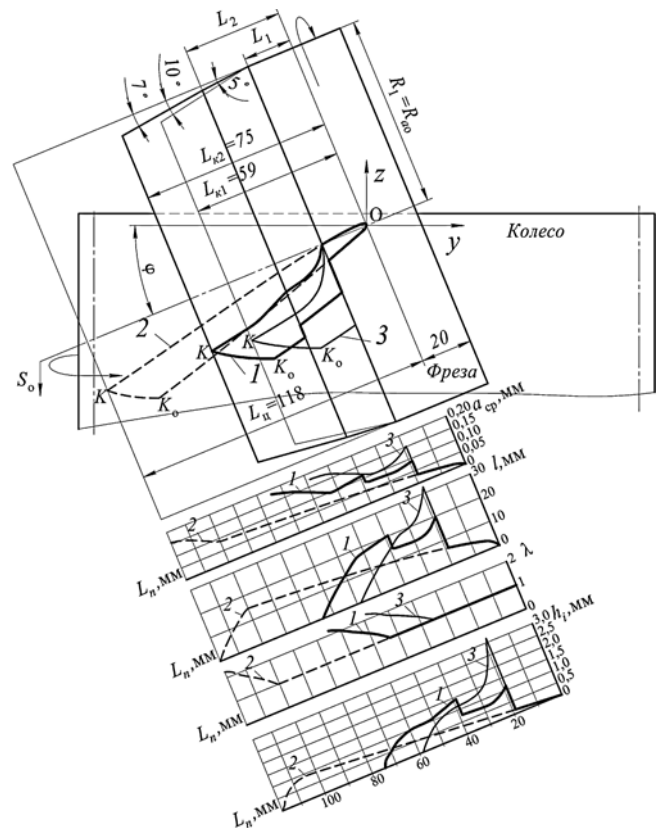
Графики зон резания, размеров срезаемых слоёв и износов зубьев червячных фрез при зубофрезеровании: 1 — для фрезы с двумя заборными конусами ($\psi_1 = 5^\circ$ и $\psi_2 = 7^\circ$); 2 — для фрезы без заборной части; 3 — для фрезы с одним заборным конусом $\psi_1 = 10^\circ$
